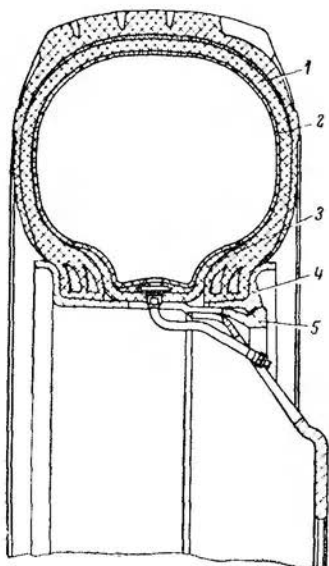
Конструкция колеса с шиной в сборе автомобиля ГАЗ-53А:
